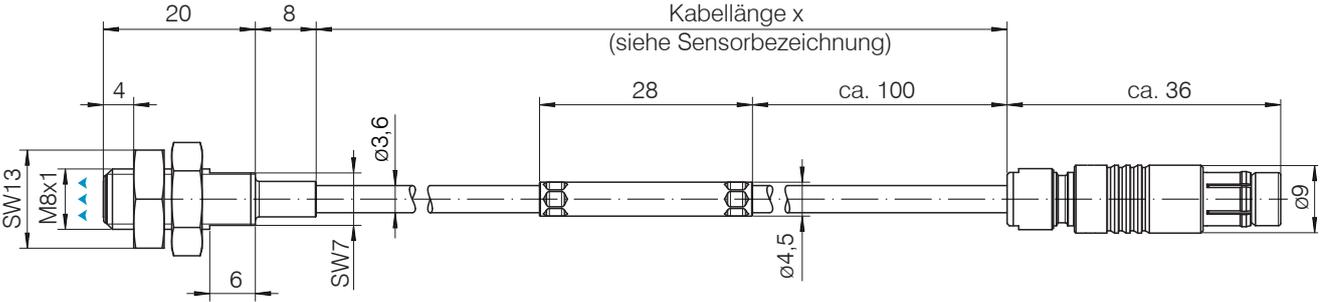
Maßzeichnung Sensoren ES-S1-C-CAX/mB0, Abmessung in mm
